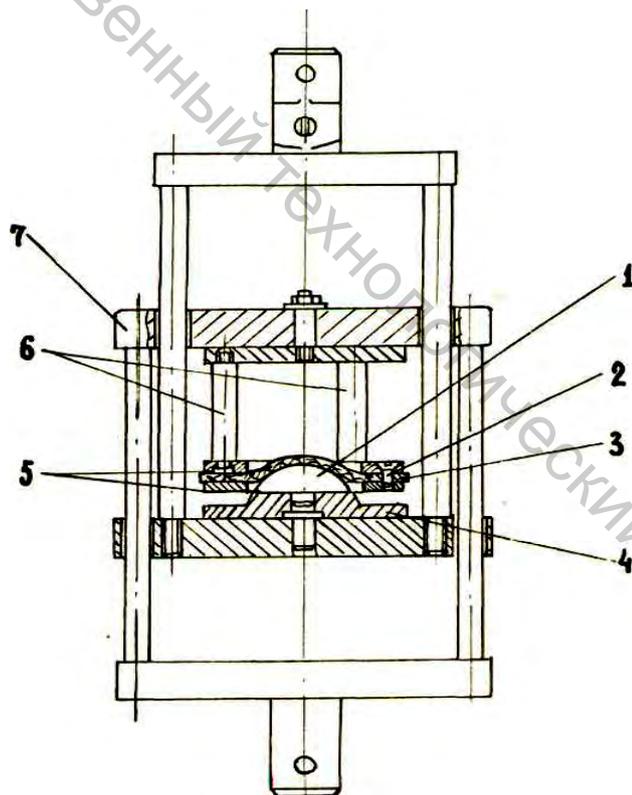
Приспособление для двухосного растяжения образцов
